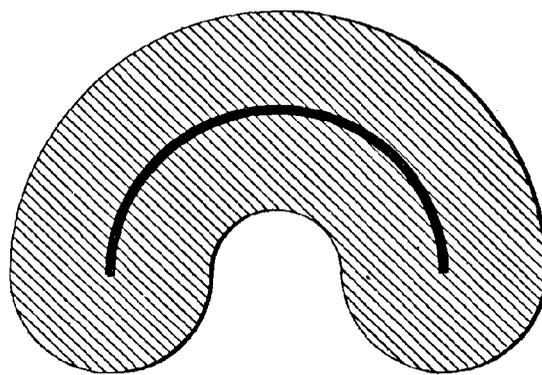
Tube Serpollet. Coupe, grandeur d'exécution.
